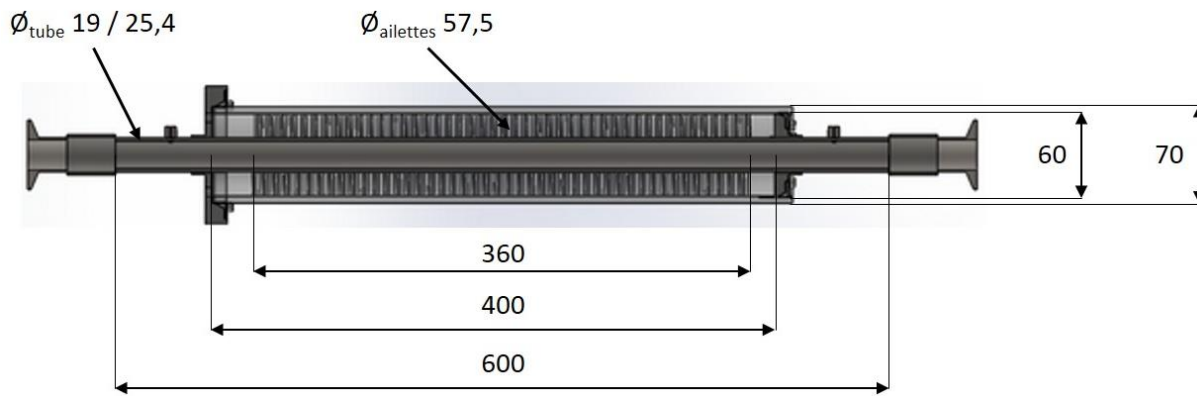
Principales dimensions du tube ailetté 7 fpi. Les valeurs sont en millimètres.
